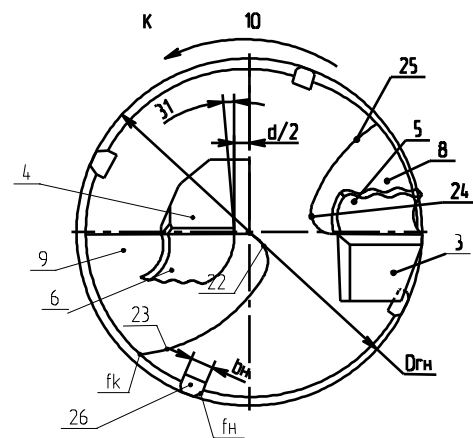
Вид на резцовую головку по стрелке K с исполнением 3 корпуса.
